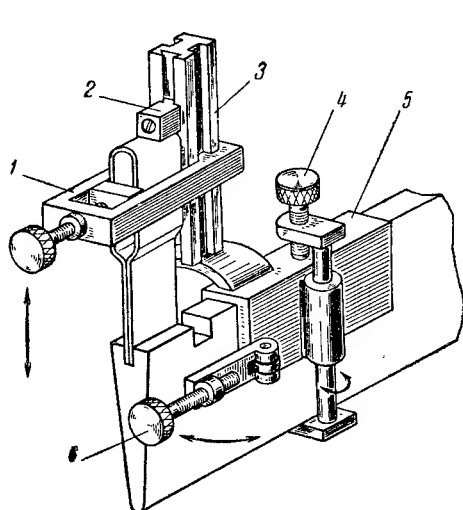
Приспособление для установки петушка и пластины при пайке припоем ПМФ7:
